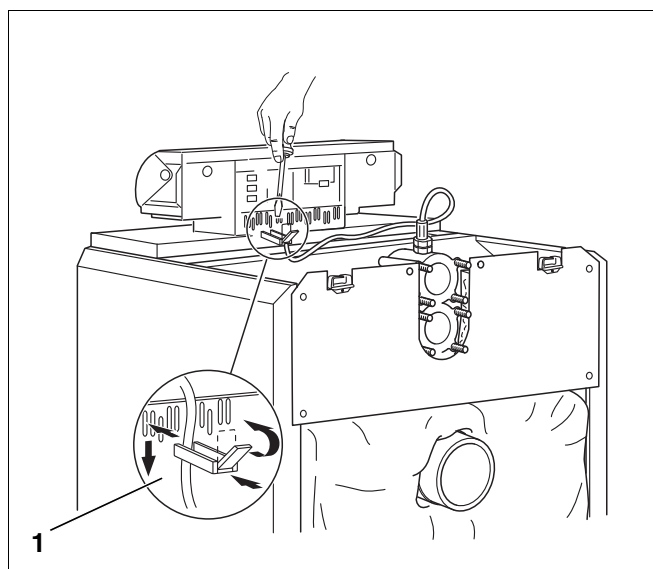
Fissaggio dei cavi di collegamento elettriche
